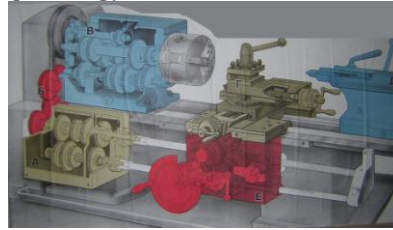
Механізми токарно-гвинторізного верстата ТГ-6
